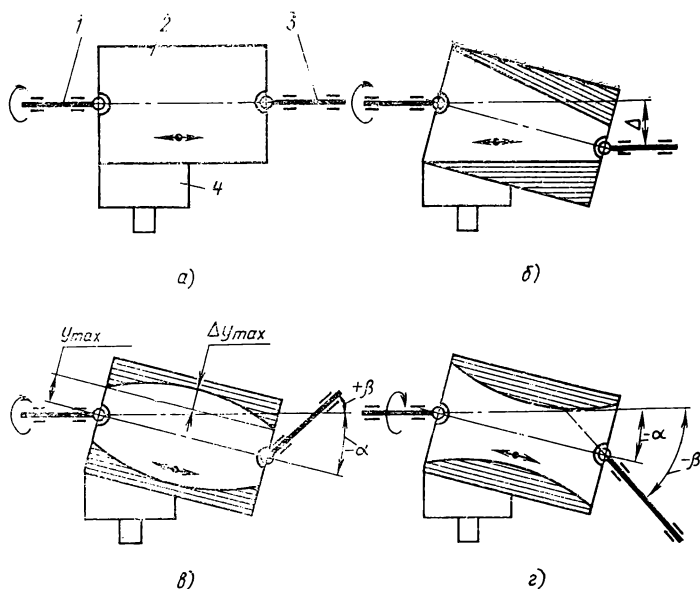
Изменение профиля цилиндрической поверхности при различных положениях звена настройки трехзвенного шарнирного механизма: а — цилиндр; б — конус; в — бочкообразность; г — седлообразность 1 — первое звено; 2 — второе звено (деталь); 3 — третье звено; 4 — инструмент
